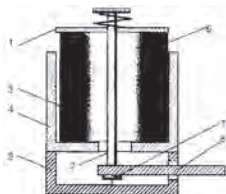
Конструктивная схема резинового виброизолятора подвесного типа: 1–крышка; 2–стержень; 3–зазор; 4–кожух; 5–корпус; 6–резиновый упругий элемент; 7–головка стержня; 8–кронштейн для крепления к опорной поверхности станка.
